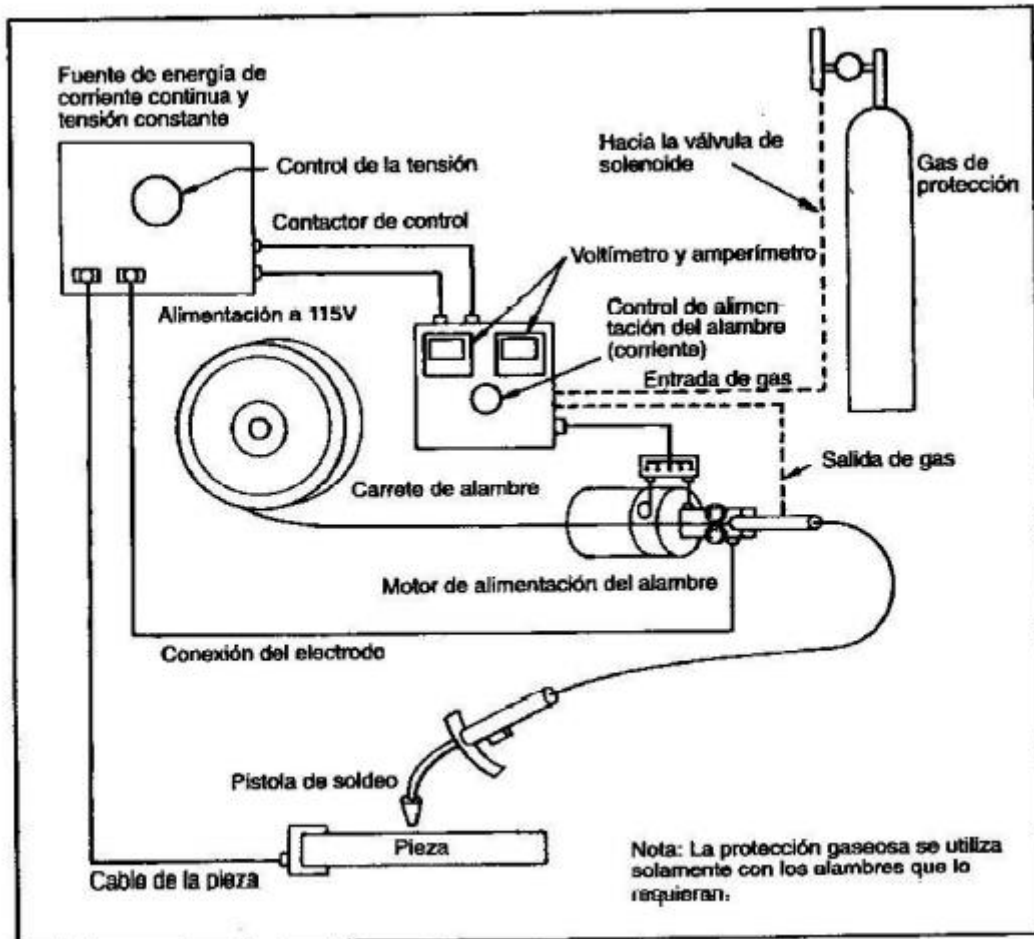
EQUIPO PARA EL SOLDEO POR ARCO CON ALAMBRE TUBULAR
